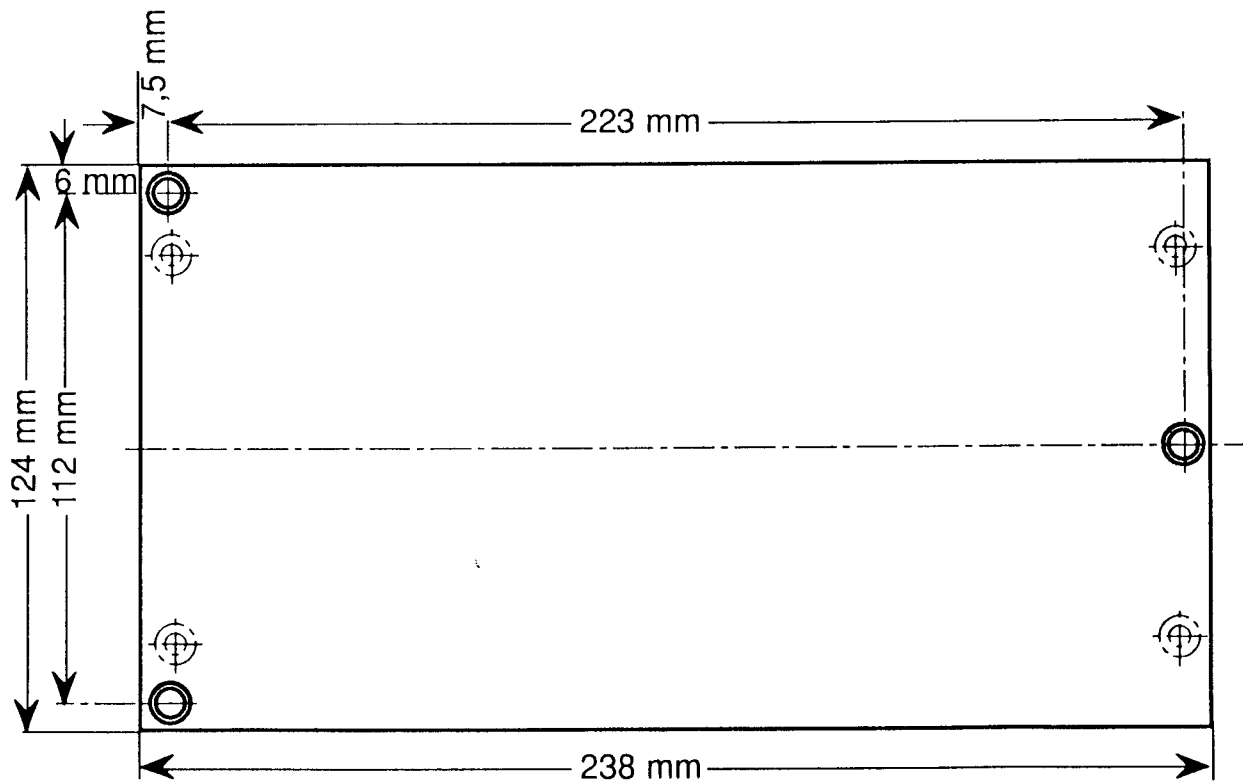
, Montagebohrungen der WA-23-Montageplatte
